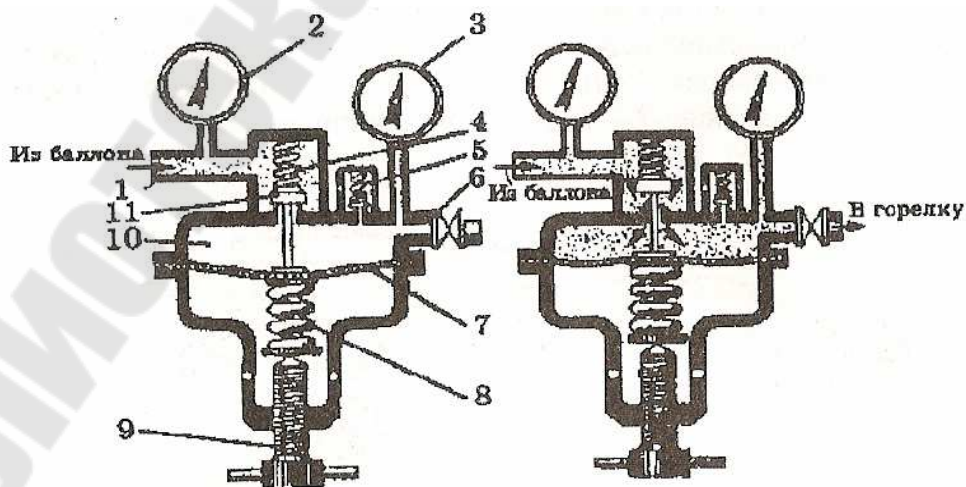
Схема газового редуктора: а – нерабочее положение; б – рабочее положение
